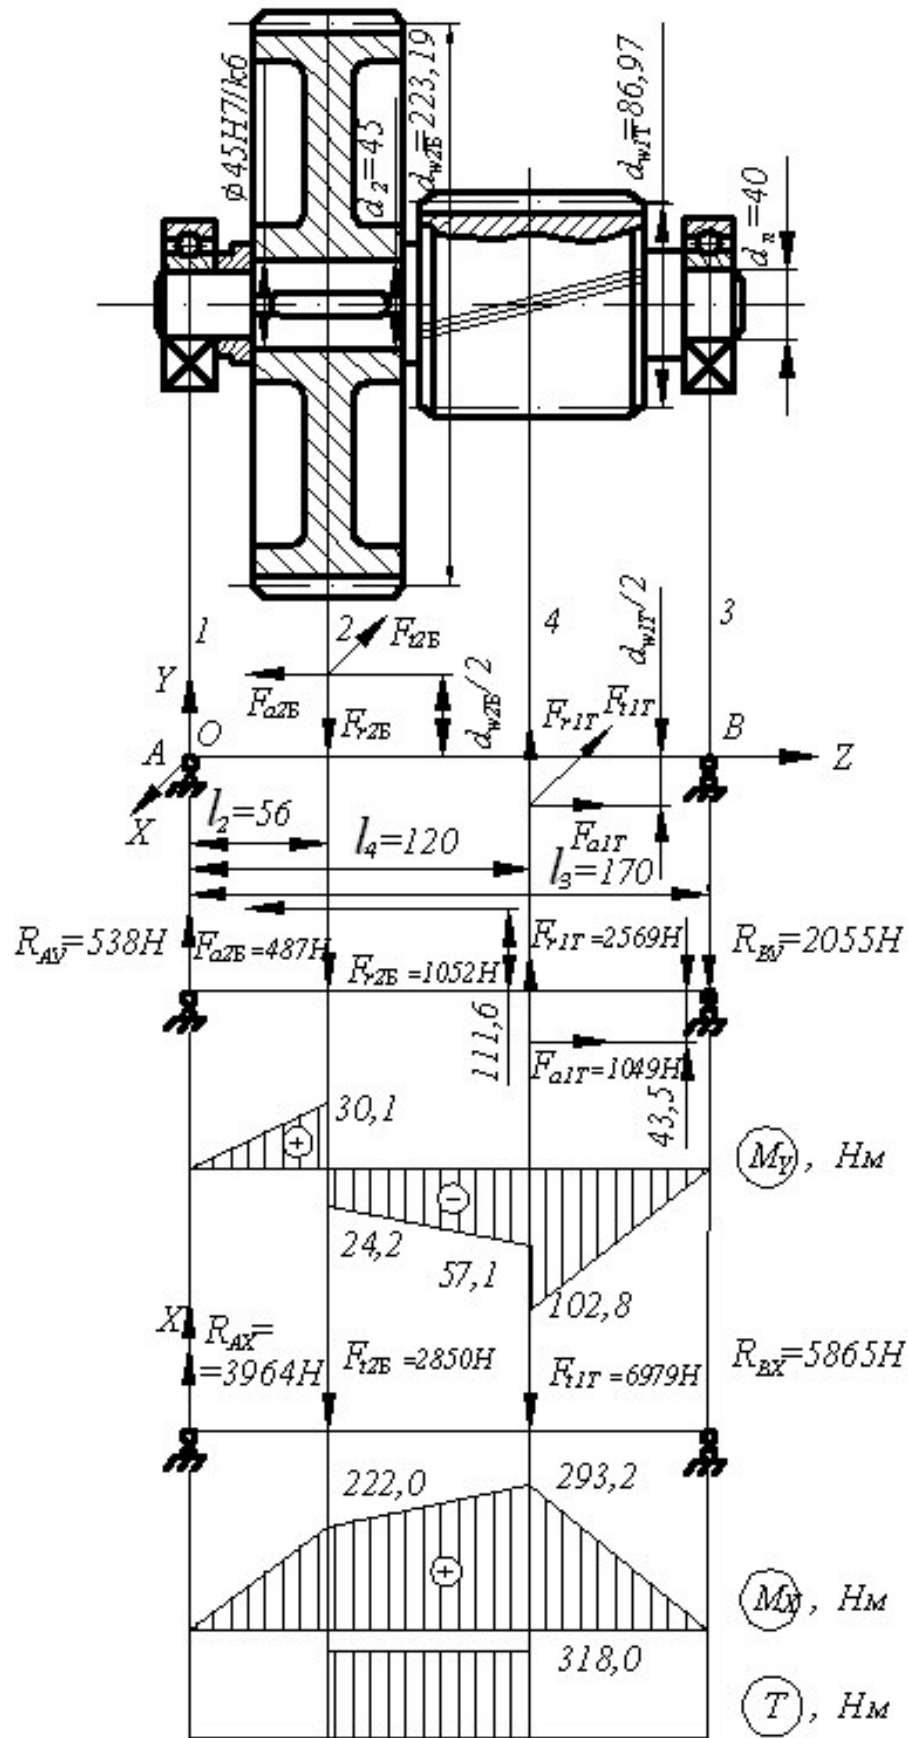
Схема к расчету промежуточного вала цилиндрического двухступенчатого редуктора по развернутой схеме
